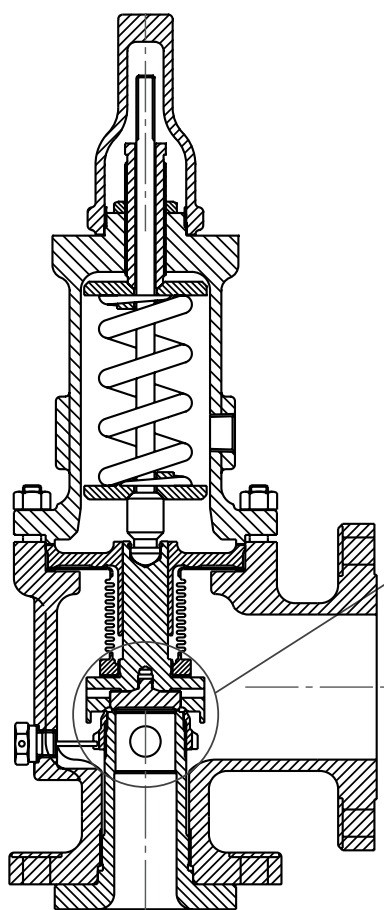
constructie van V- en W-doorstroomkleppen
